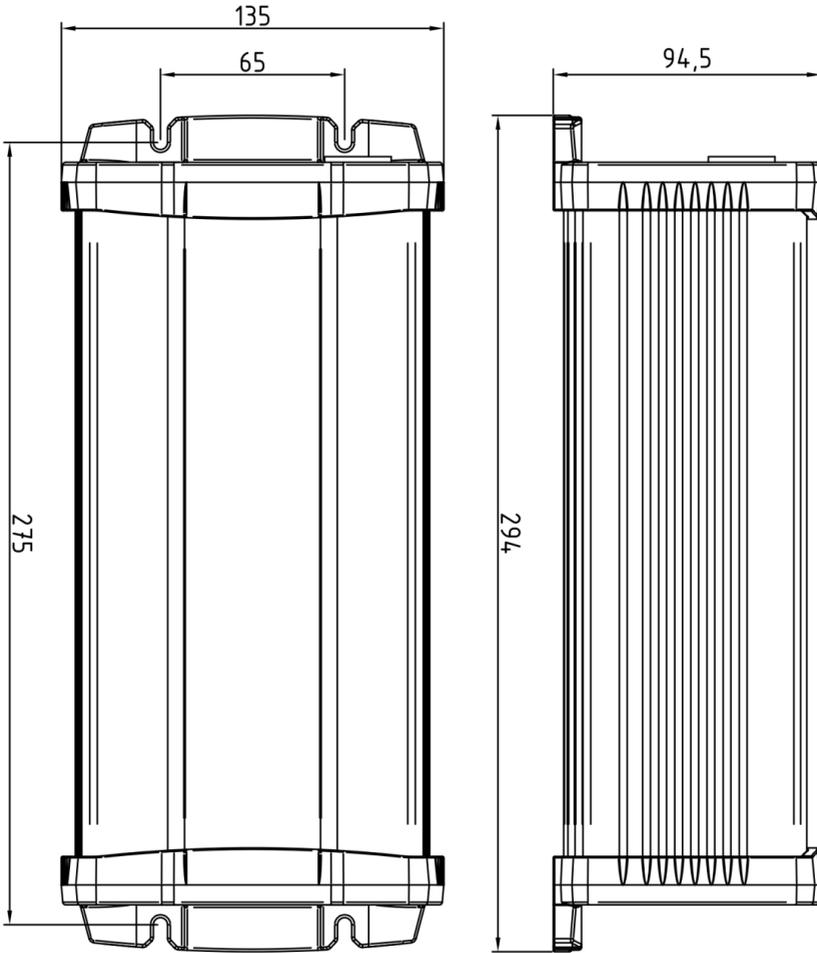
Maßzeichnung Ladegerät PWC in mm
